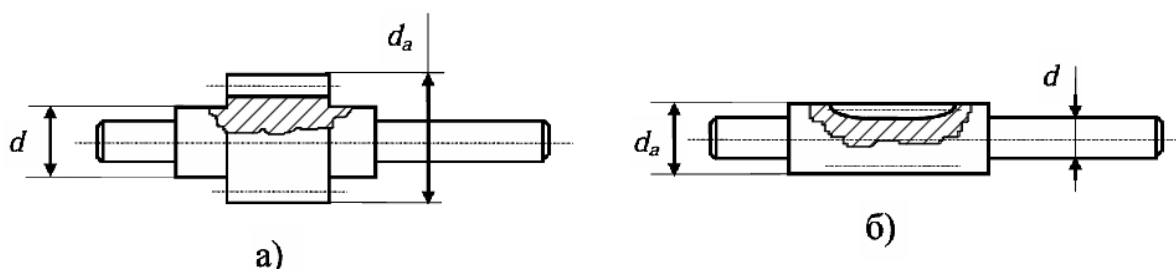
Конструктивные схемы вала-шестерни
